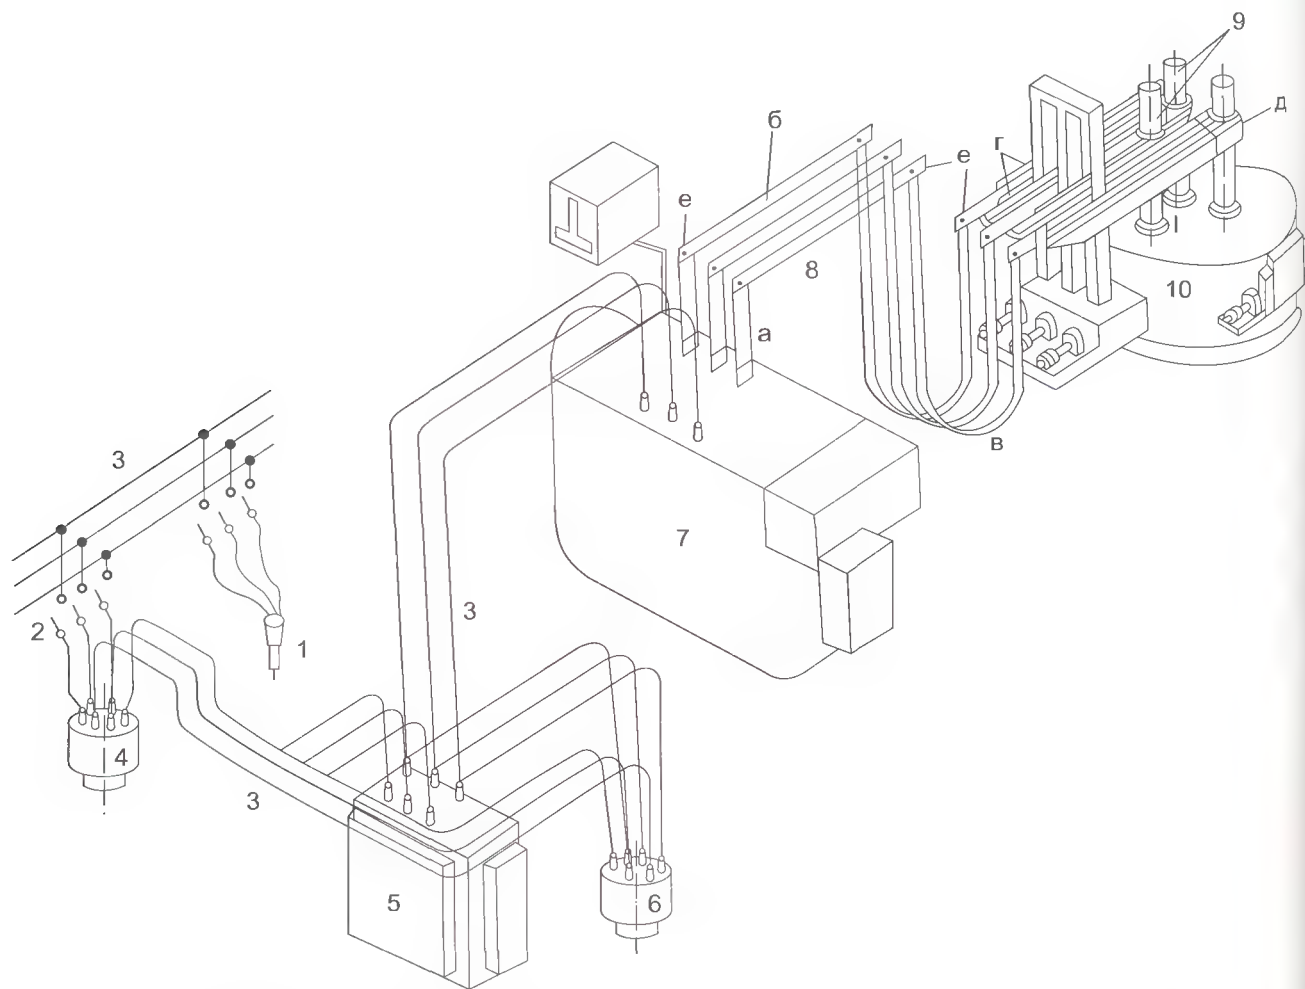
Схематический чертеж дуговой сталеплавильной печи
